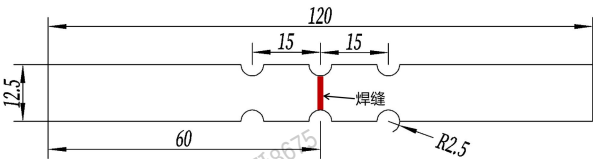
焊缝韧性评价试样示意图及尺寸（mm）
